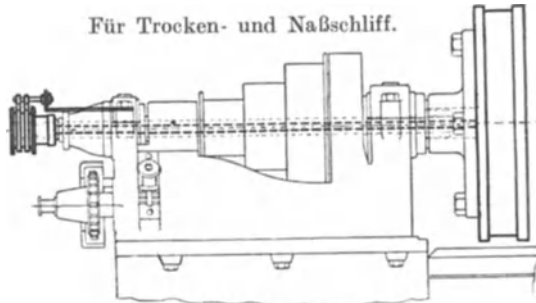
Anschluß des Rundfutters bei einer Maschine mit durchbohrter Spindel.
